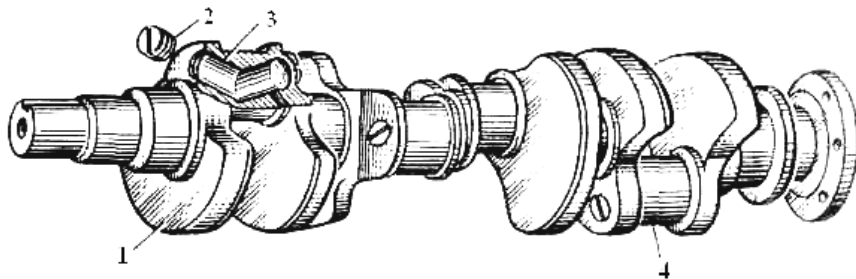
Колінчатий вал автомобіля ЗІЛ-130
